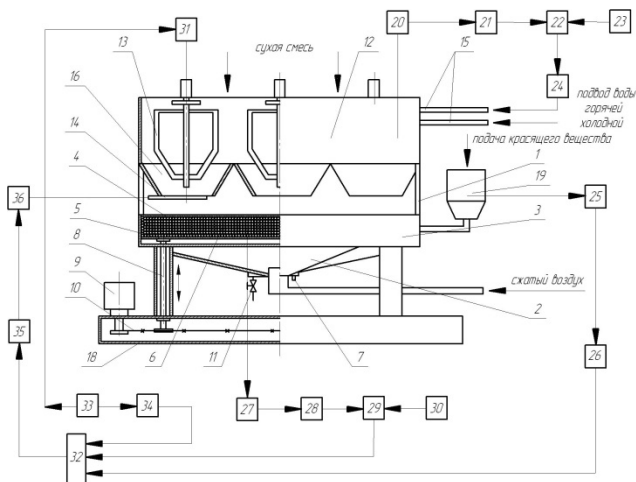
Автоматизированный технологический комплекс для мелкосерийного производства строительного декора из гипса: 1 – корпус; 2 – пневмокамера; 3 – пневмочейка; 4,5 – пластины; 6 – зернистый слой; 7 – перепускной клапан; 8 – шток; 9,31,36 – электродвигатели; 10 – цепная передача; 11 – вентиль; 12 – бункер; 13 – якорные мешалки; 14 – заслонка; 15 – патрубки для подачи воды; 16 – дозирующее устройство; 17 – форсунка; 18 – станина; 19 – емкость с красящим веществом; 20 – температурный датчик; 21,28 – вторичный прибор; 22 – регулятор сигнала; 23,30 – задатчик; 24 – исполнительный механизм; 25 – емкостный датчик уровня; 26 – электронный сигнализатор уровня; 27 – датчик давления; 29 – регулятор; 32 – логический элемент «И»; 33 - схема управления электродвигателем; 34 – пороговое реле напряжения; 35 – магнитный пускатель
